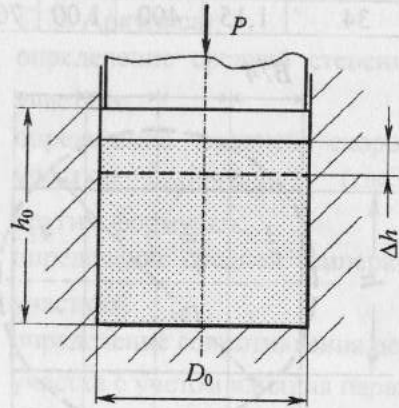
Схемы осадки пористой заготовки в закрытом штампе (матрице)
